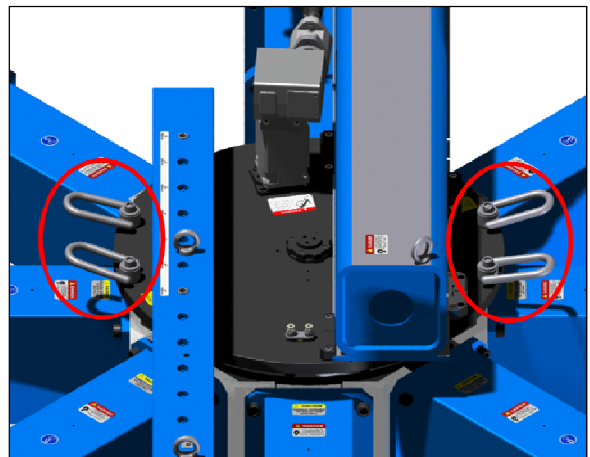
Points de levage de la machine assemblée (FF8200 illustrée)
